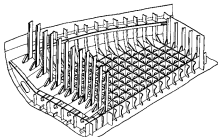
Поперечная система двойного перекрытия в трюме рулевого (конец второго дна и обшивка поперечной переборки не показаны)
